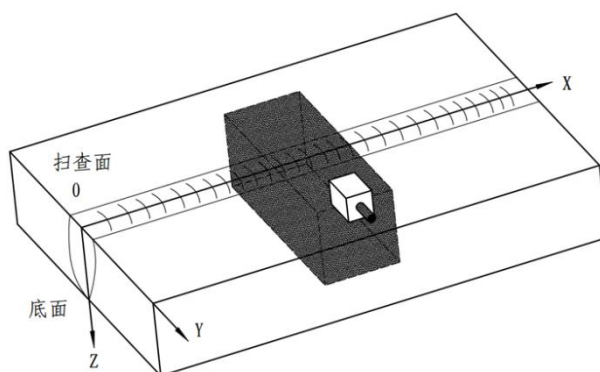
焊接接头检测全聚焦 3D 型显示
